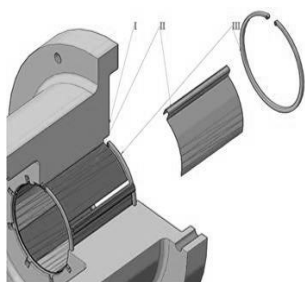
Лепестковый опорный газодинамический подшипник:
